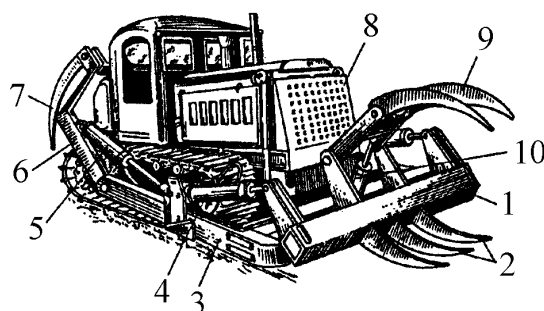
Корчеватель-собиратель КСП-20: 1 – балка передняя; 2 – корчующие клыки; 3 – рама; 4, 5, 10 – гидроцилиндры; 6 – боковина; 7 – механизм подрезки корней; 8 – щит; 9 – зубья
